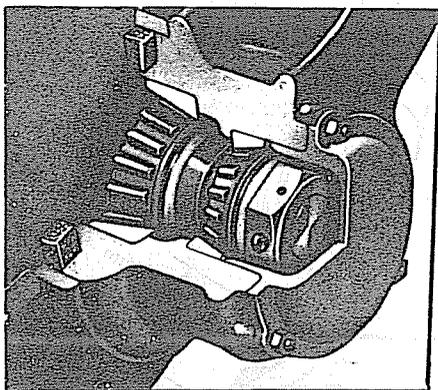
Maza de los rodamientos, con cojinetes de rodillos cónicos.
